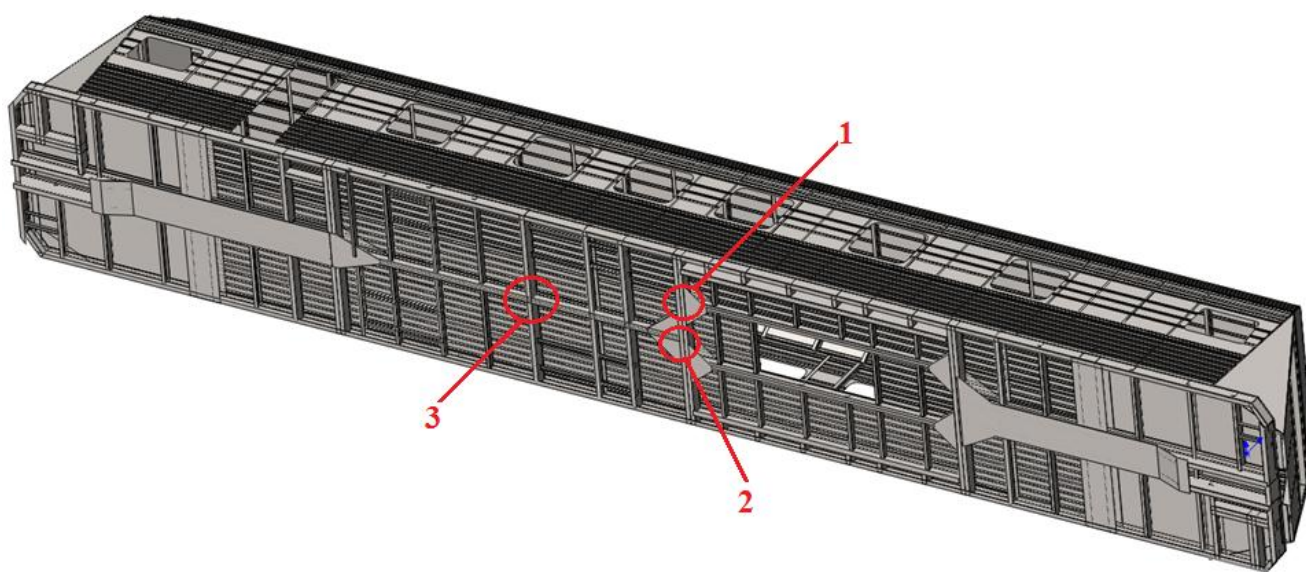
Схема размещения наиболее нагруженных зон несущей конструкции кузова автотрисы: 1 – зона соединения продольной балки рамы кузова с поперечной балкой в месте монтажа силовой установки; 2 – зона соединения хребтовой балки рамы кузова с поперечной балкой в месте монтажа силовой установки; 3 – зона соединения хребтовой балки рамы кузова с поперечной балкой
